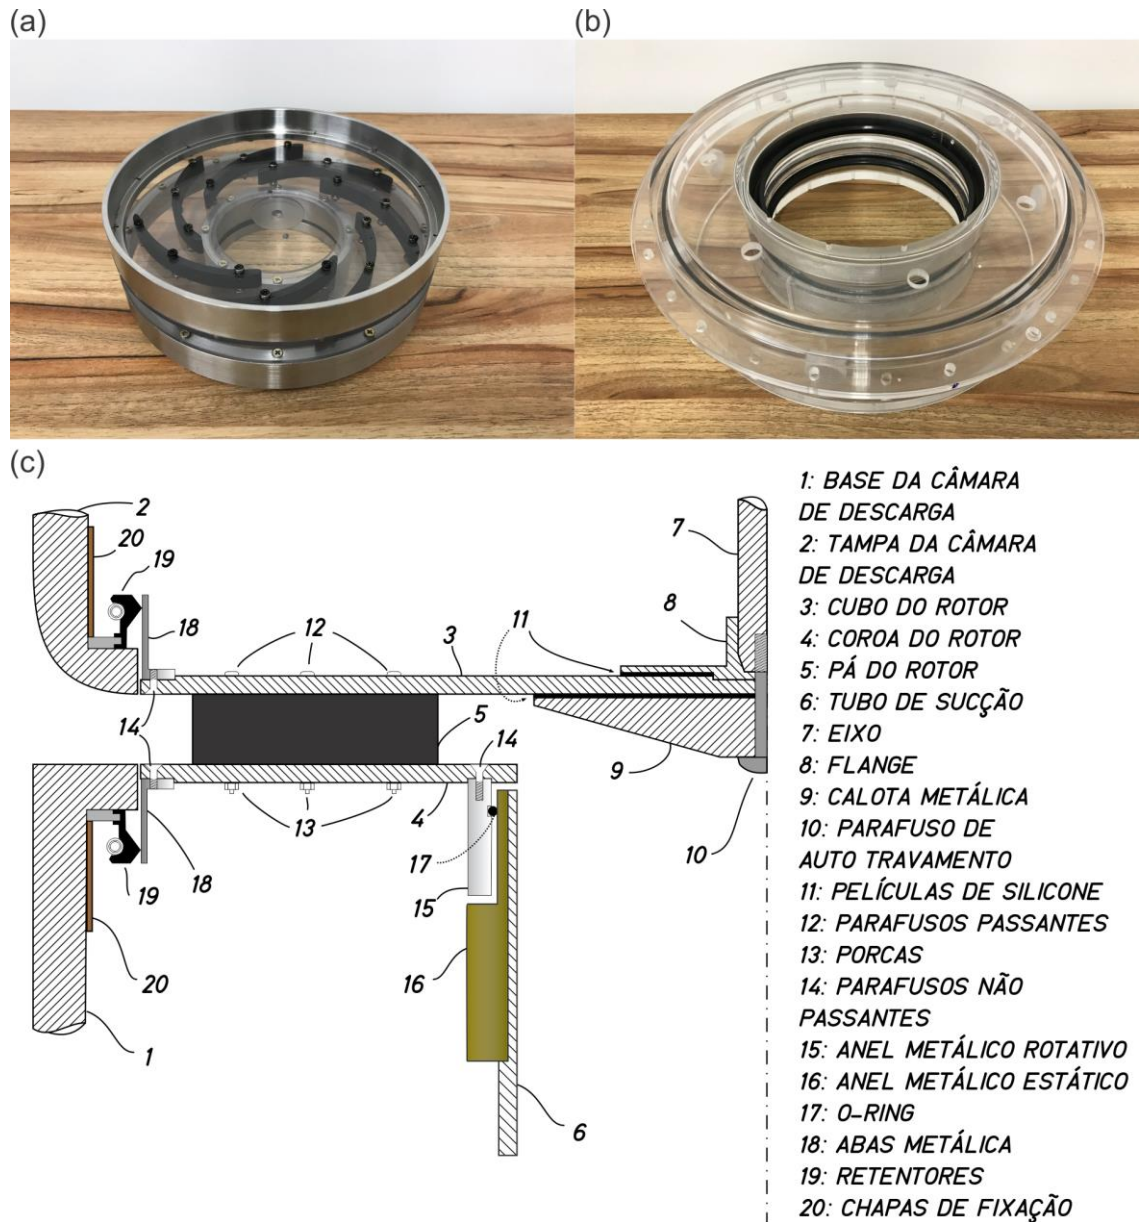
(a) Rotor; (b) Câmara de descarga; (c) Montagem;
